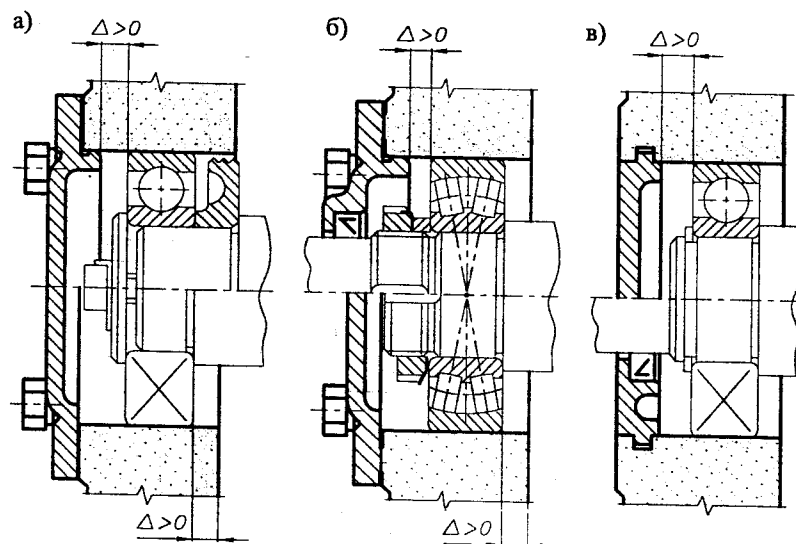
Установка наружного кольца неразъемного подшипника в корпусе плавающей (самоустанавливающейся) опоры
